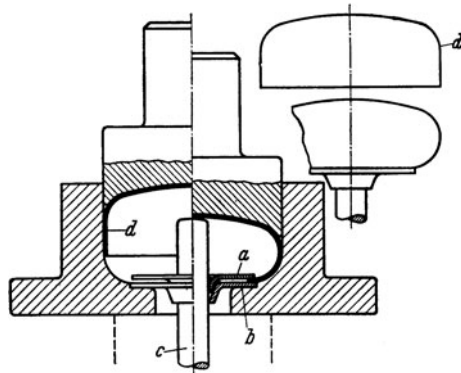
Innenbördelwerkzeug zur Befestigung runder balliger Handgriffe
